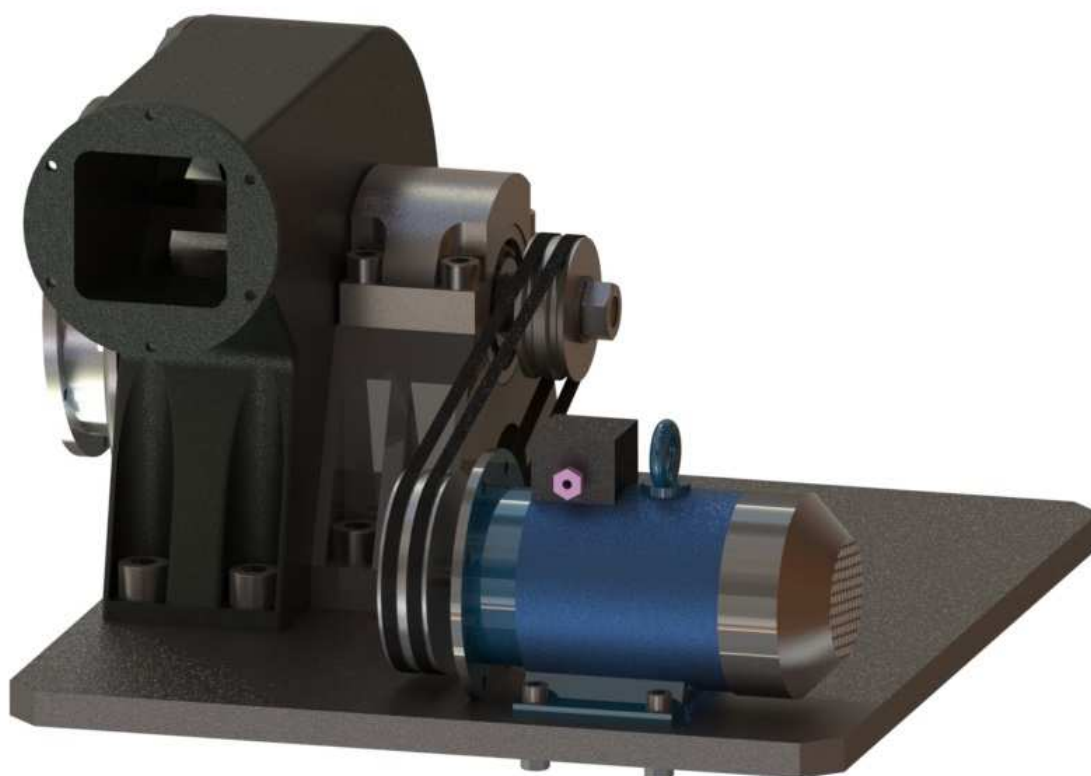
3D модель зборки вентилятора (вид 2).
